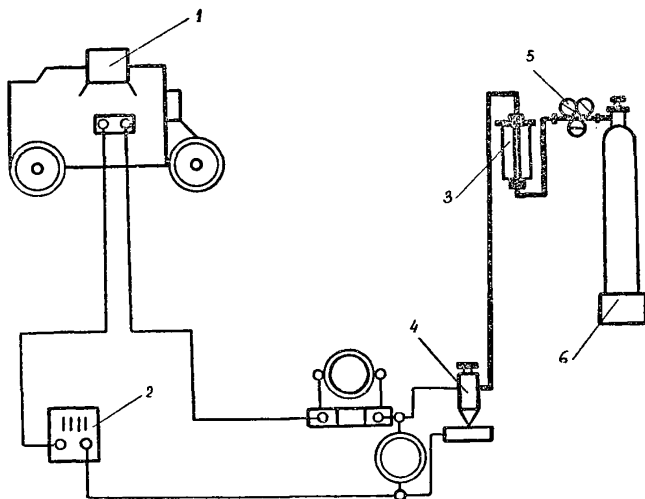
Схема поста аргоно-дуговой сварки:
